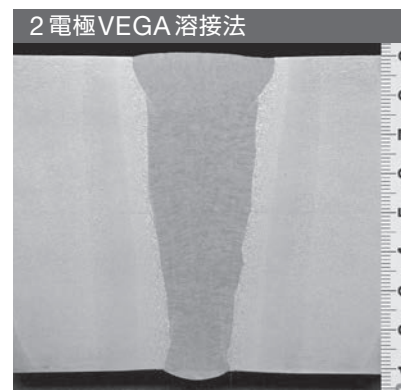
2電極VEGA溶接法の溶接継手の断面マクロ (板厚80mm)
